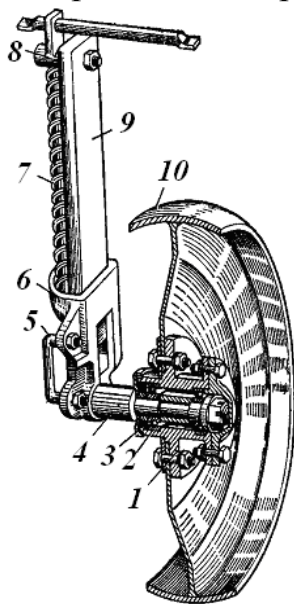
Опорне колесо: 1 - маточина, 2 - шарикопідшипник; 3 - ковпак; 4 - піввісь; 5 - хомут; 6 - тримач; 7 - гвинт; 8 - гайка; 9 - стояк; 10 - обід
